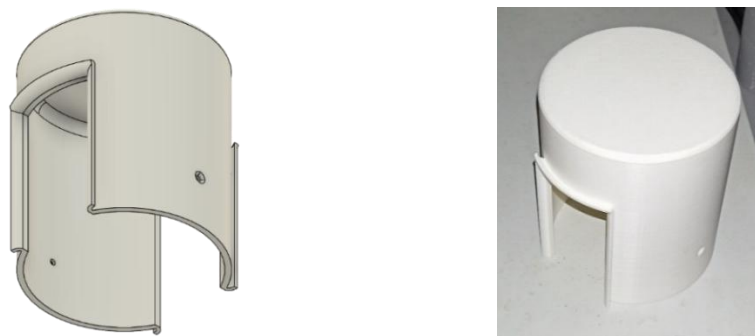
Усовершенствованный вариант верхней части защитного корпуса с элементами отвода воды: 3D-модель (слева) и изготовленный образец (справа)
